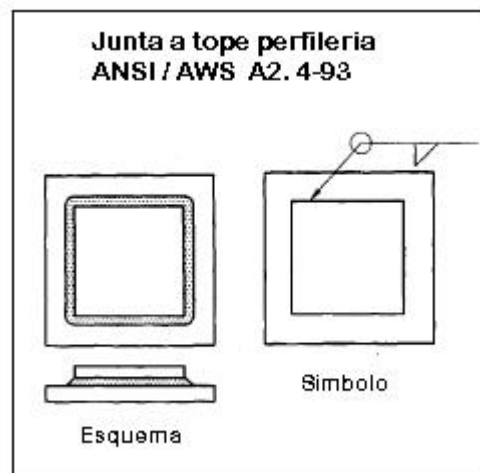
Tipo de Soldadura a emplearse
